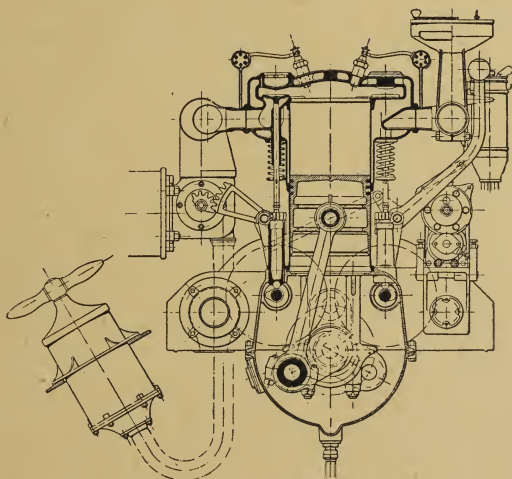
Querschnitt des Maybach-Luftschiff-Motors.
